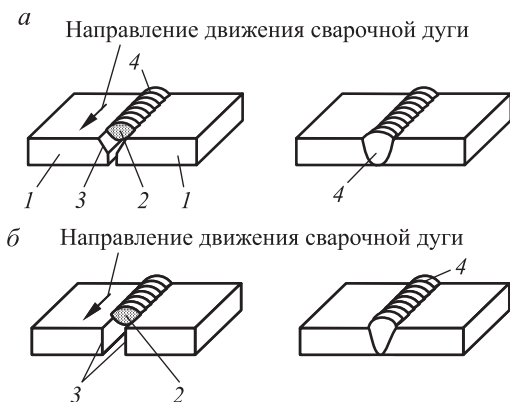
Процесс соединения деталей сваркой плавлением:
